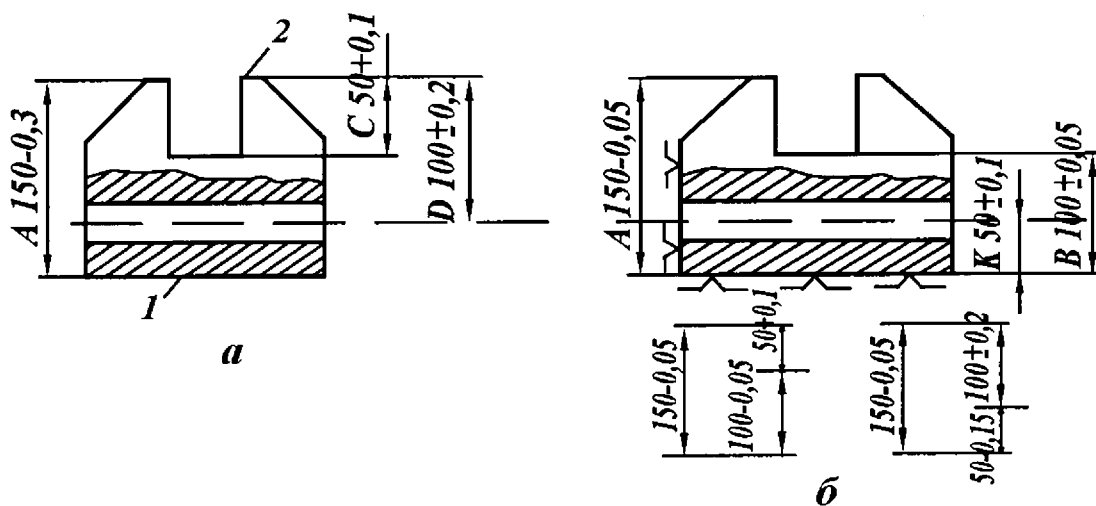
Чертеж детали (*а*) и эскиз обработки (*б*)
